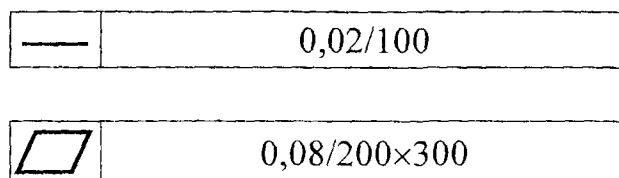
Примеры условных обозначений допусков формы поверхностей формы и расположения
